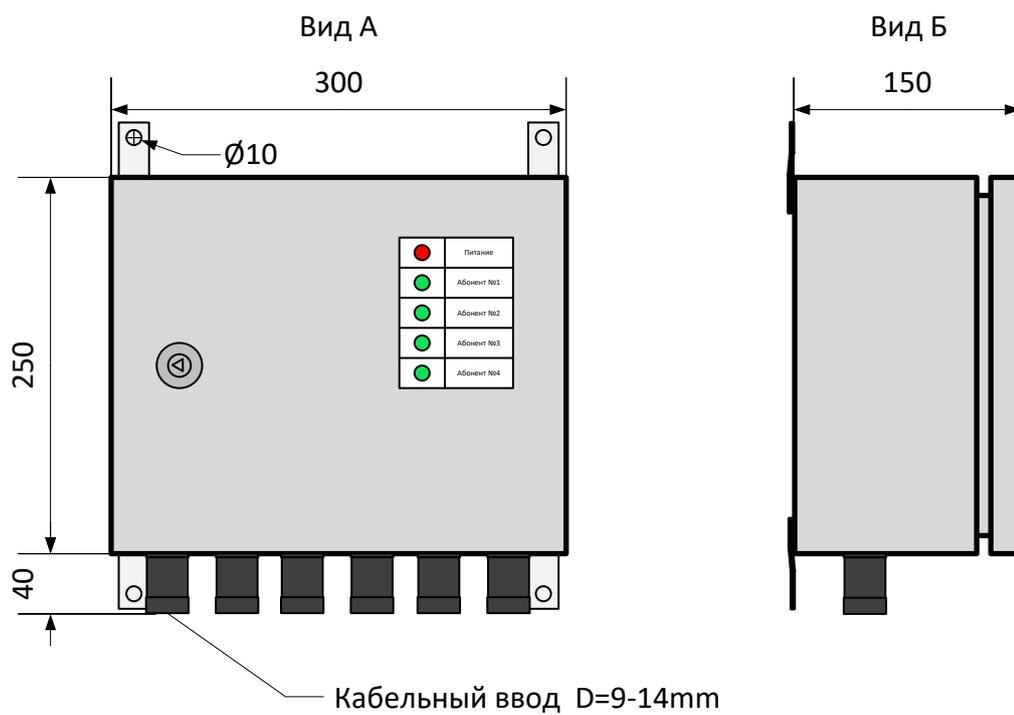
Внешний вид и габаритные размеры базового блока УПК-4.
